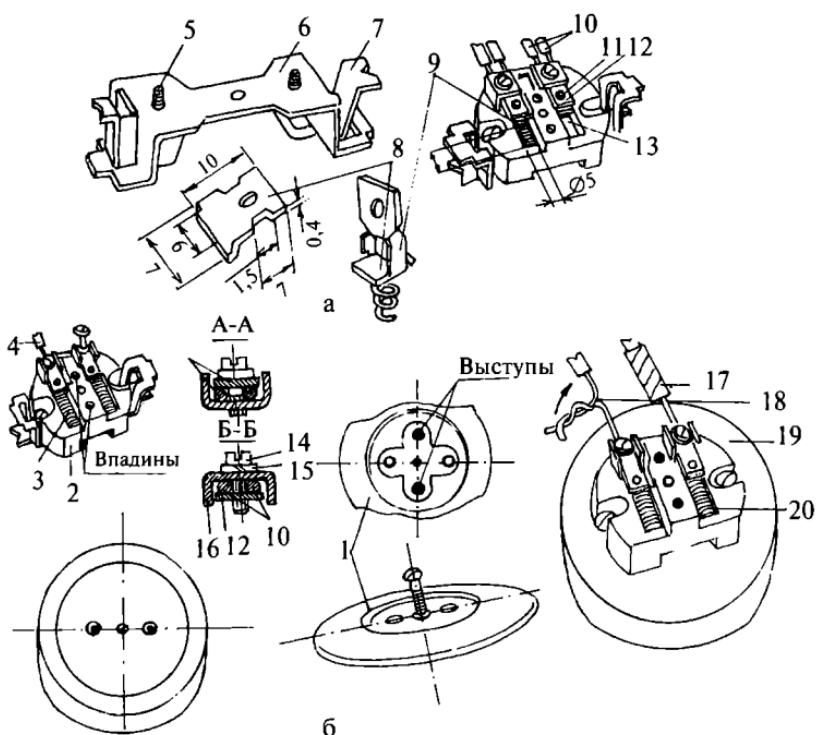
Розетка с гнездами из пластин и пружин: а — для скрытой проводки; б — для открытой проводки; 1 — крышка; 2 — основание; 3 — пружина; 4 — проводник; 5 — винт скобы; 6 — скоба; 7 — распорная лапка; 8 — пластина; 9 — направляющая; 10 — проводники; 11 — винт клеммы; 12 — клемма; 13 — ремонтная временная направляющая; 14 — винт; 15 — шайба разрезная; 16 — шайба квадратная; 17 — изоляционная лента; 18 — скрутка жил; 19 — подрозетник; 20 — закладная гайка
